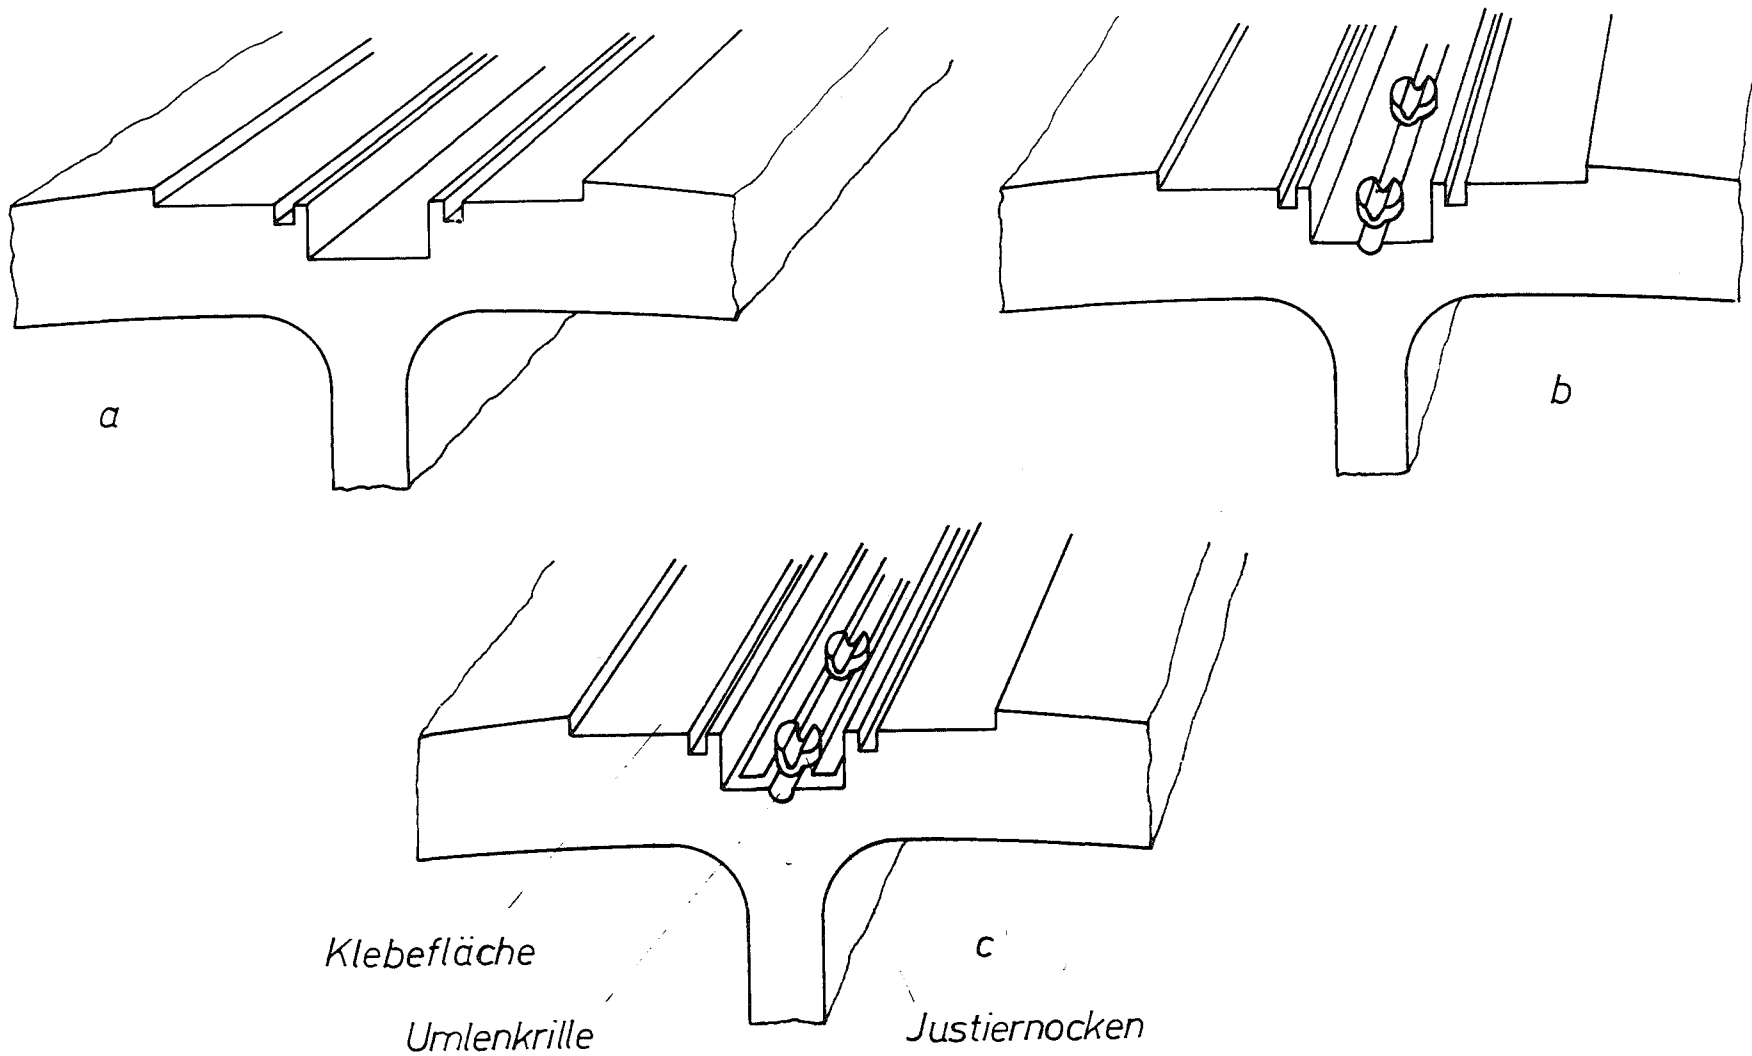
Die wesentlichen Bearbeitungsschritte bei der Fertigung des Gasführungsrohres mit eingearbeiteter Umlenkrille und aufgesetzten Justiernocken
